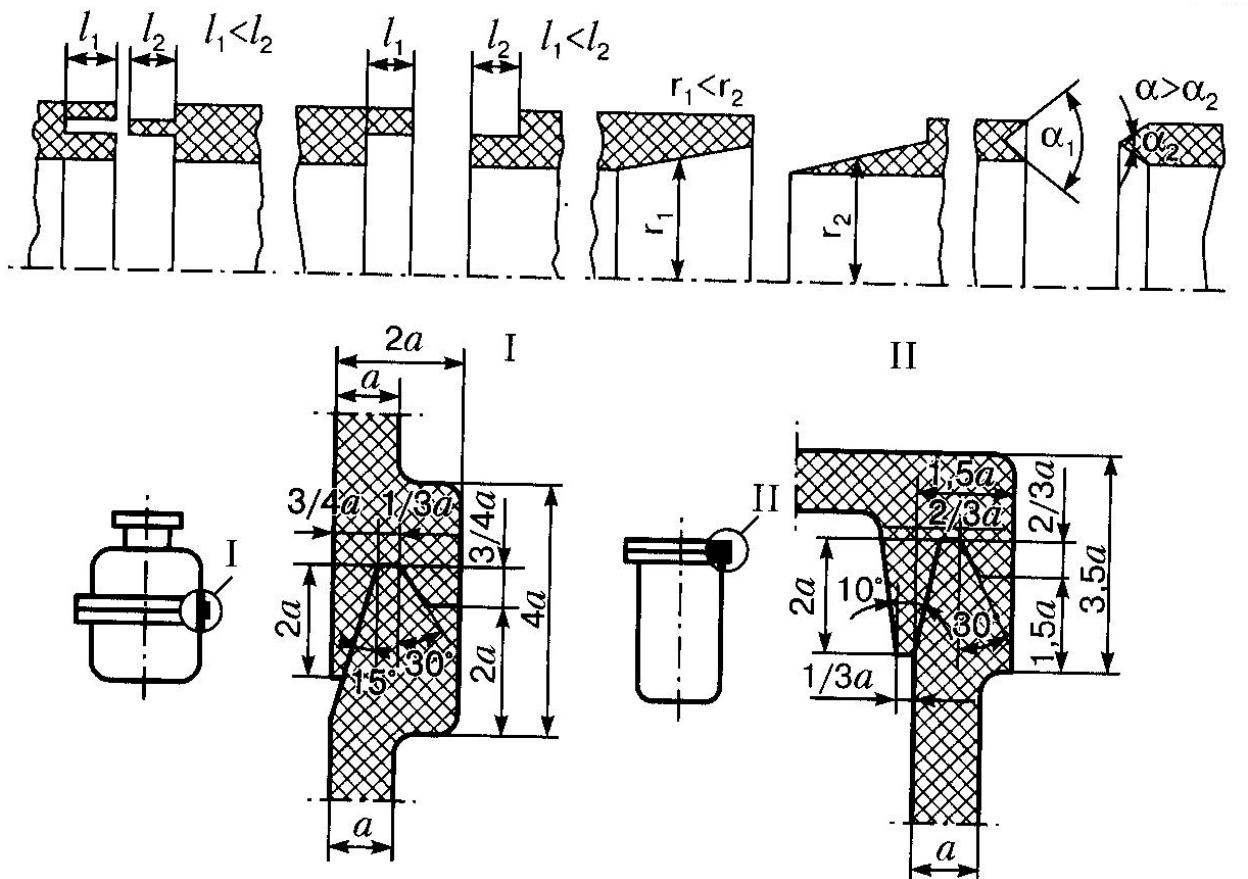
Конструкції розроблення кромок труб під зварювання тертям
